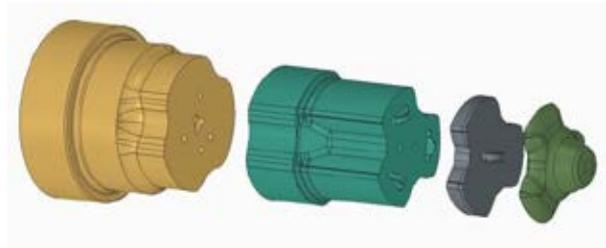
Vue éclatée du poinçon réalisé par usinage et soudage
